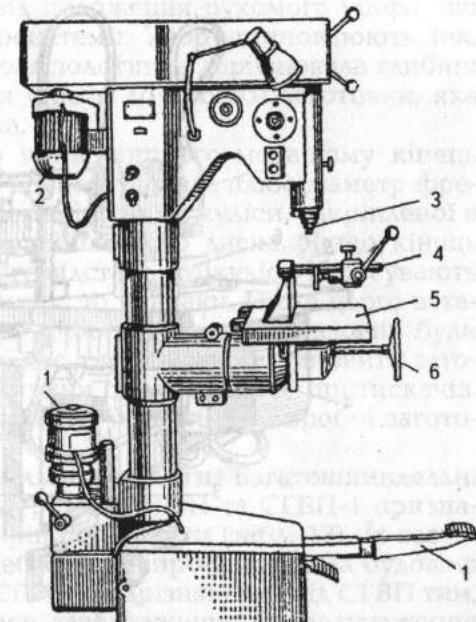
Одношпиндельний свердильно-пазувальний верстат СвА-2:
